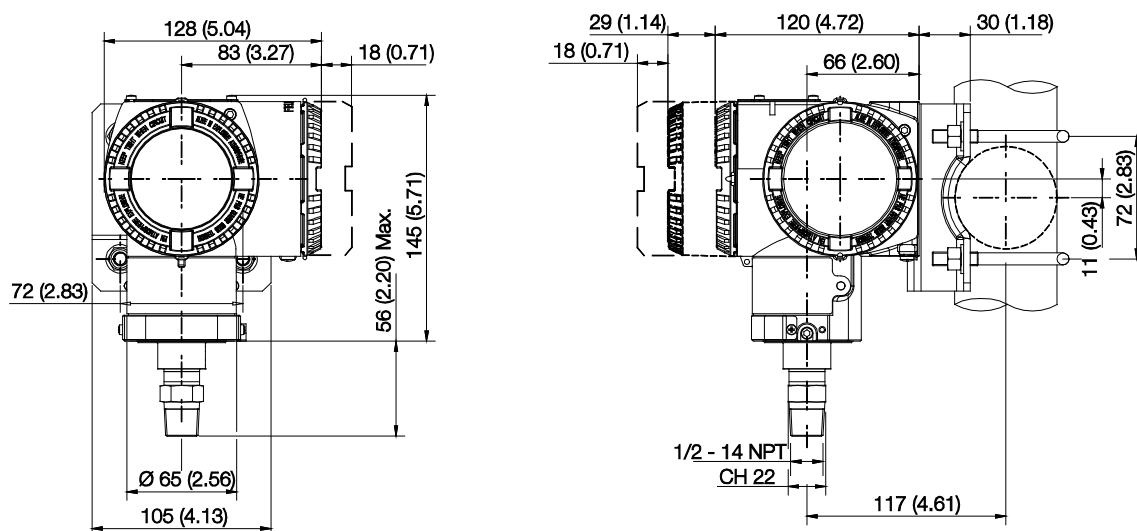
габариты - корпус типа «бочка» – внутренняя резьба 1/2 NPT
